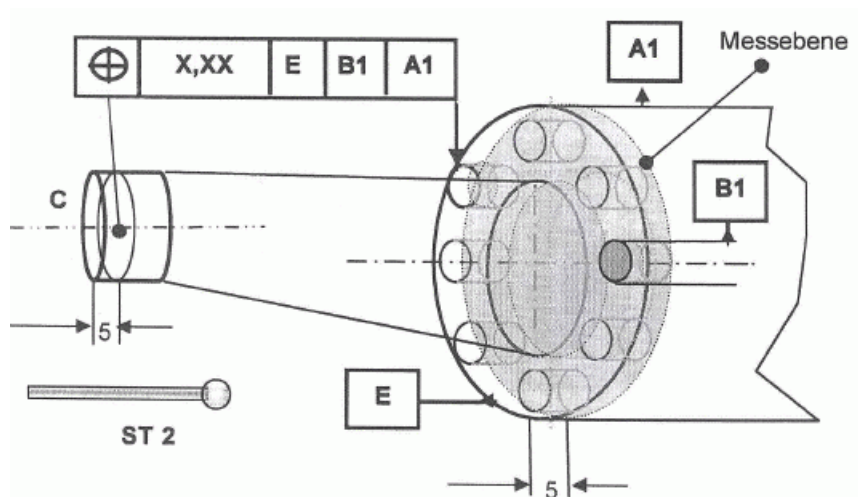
Definition der Messaufgabe für die Position der großen Mittelbohrung (C)
